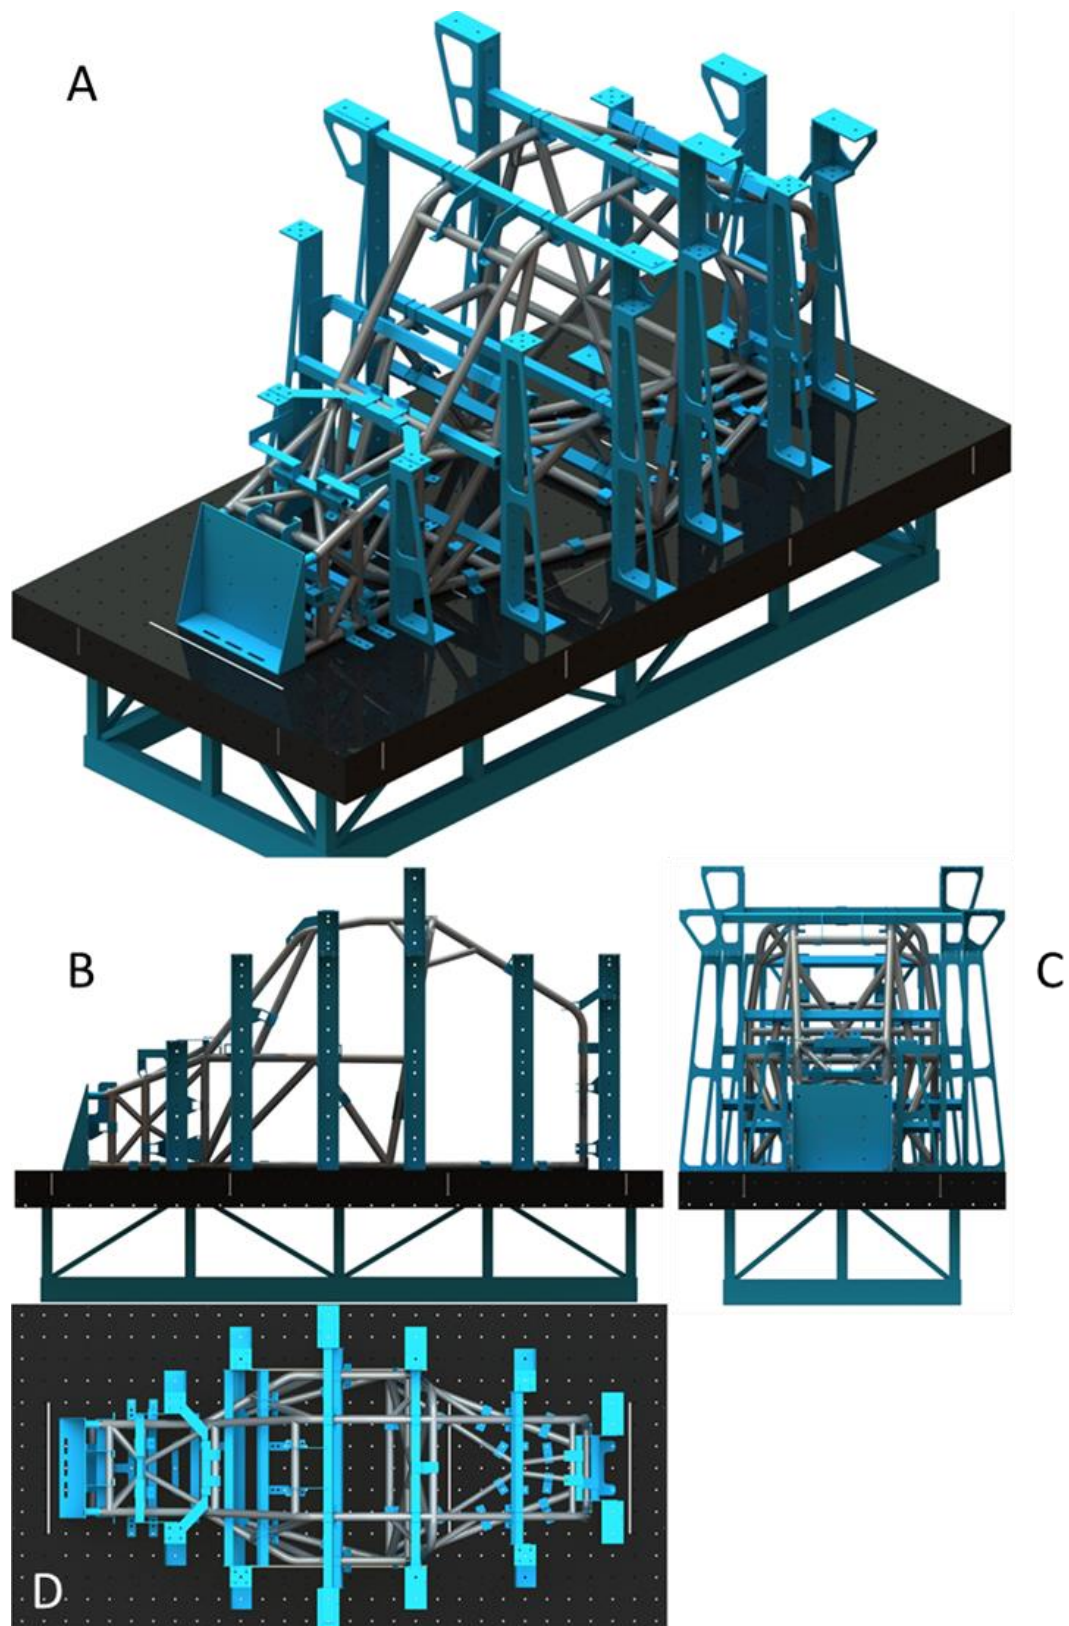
Modelação do gabarito de soldadura A vista isométrica, B vista frontal, C vista lateral D vista superior
